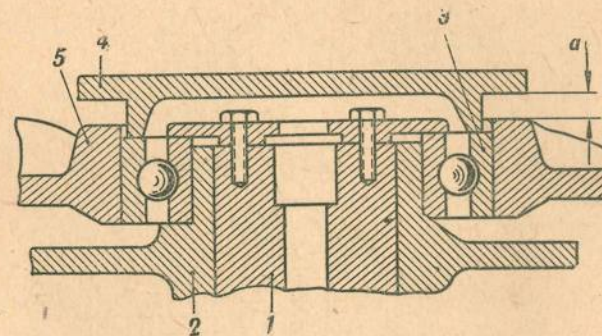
Подбор прокладок к крышке подшипника бортового редуктора:
